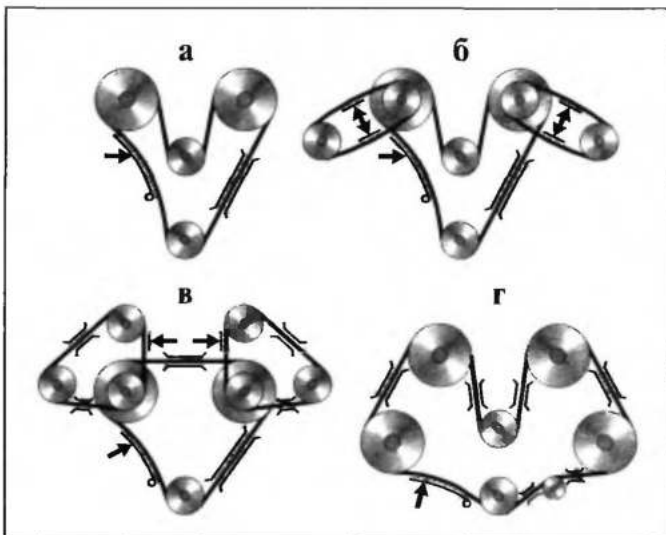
Схемы цепного привода распределительных валов V-образных двигателей:
